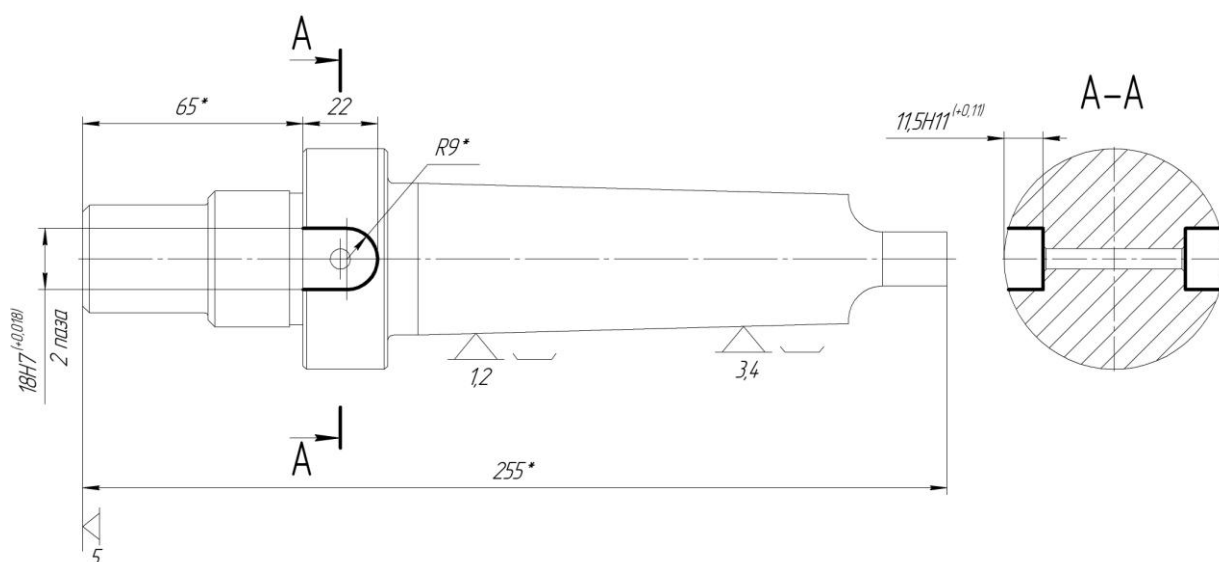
Схема базування заготовки на координатно-розточувальній з ЧПК операції (другий варіант)
